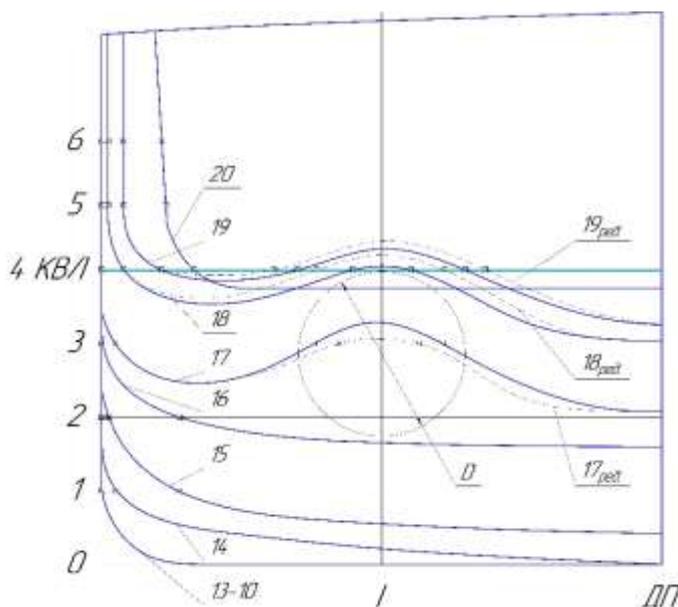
Теоретический чертёж корпуса с возможными вариантами корректировки.
